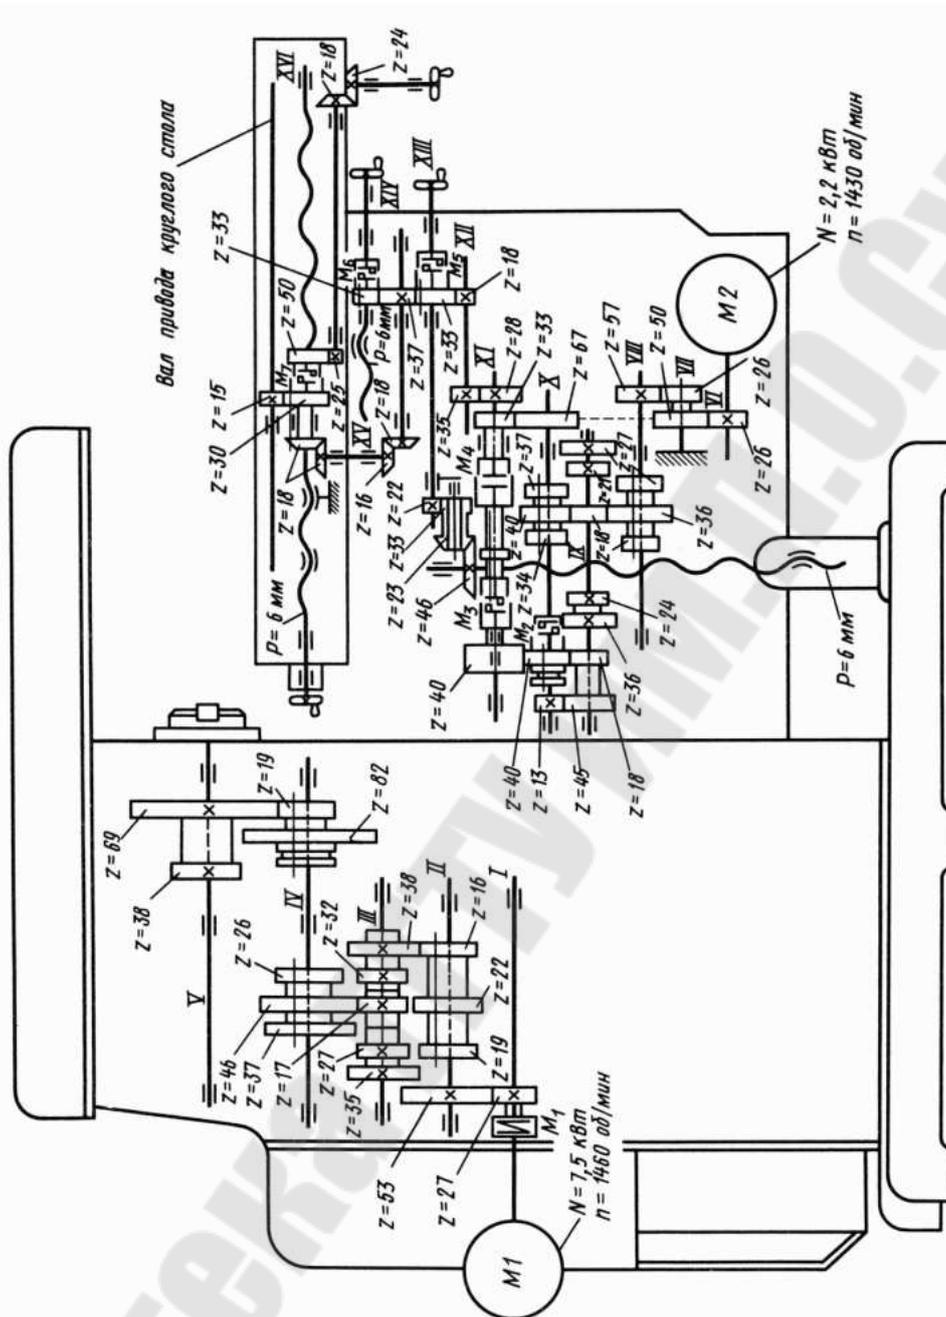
Кинематическая схема универсально-фрезерного станка 6P82
